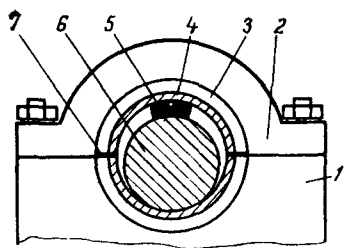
Проверка зазоров в подшипниках скольжения:
